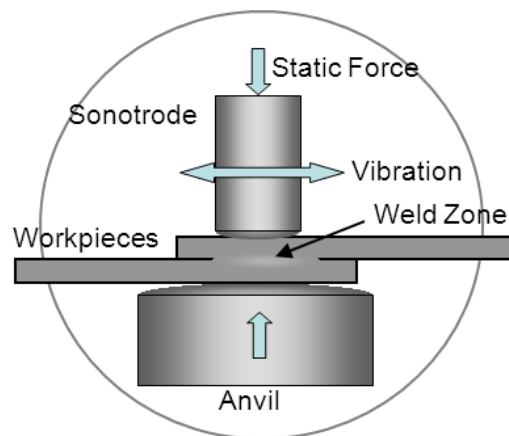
Sistema de soldadura por ultra-sons
